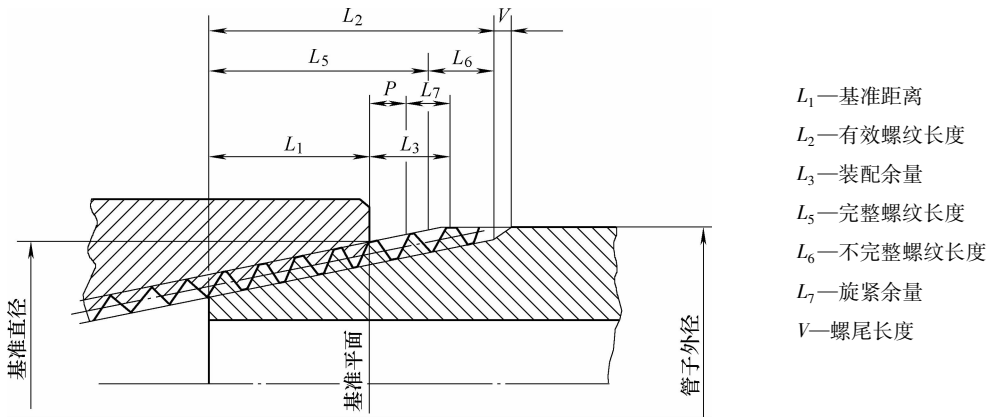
圆锥外螺纹各主要尺寸的分布位置
